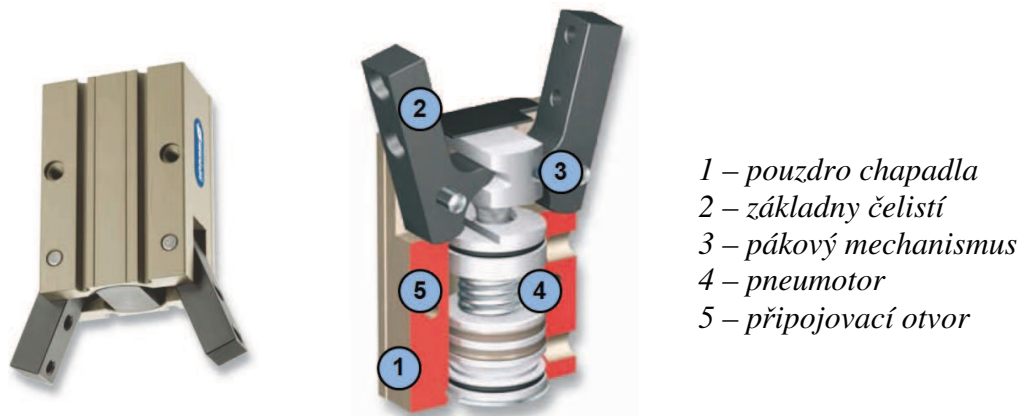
2-čelist'ové paralelní pneumatické chapadlo SCHUNK JGP s klínovým mechanismem a jeho hlavní části [12]
